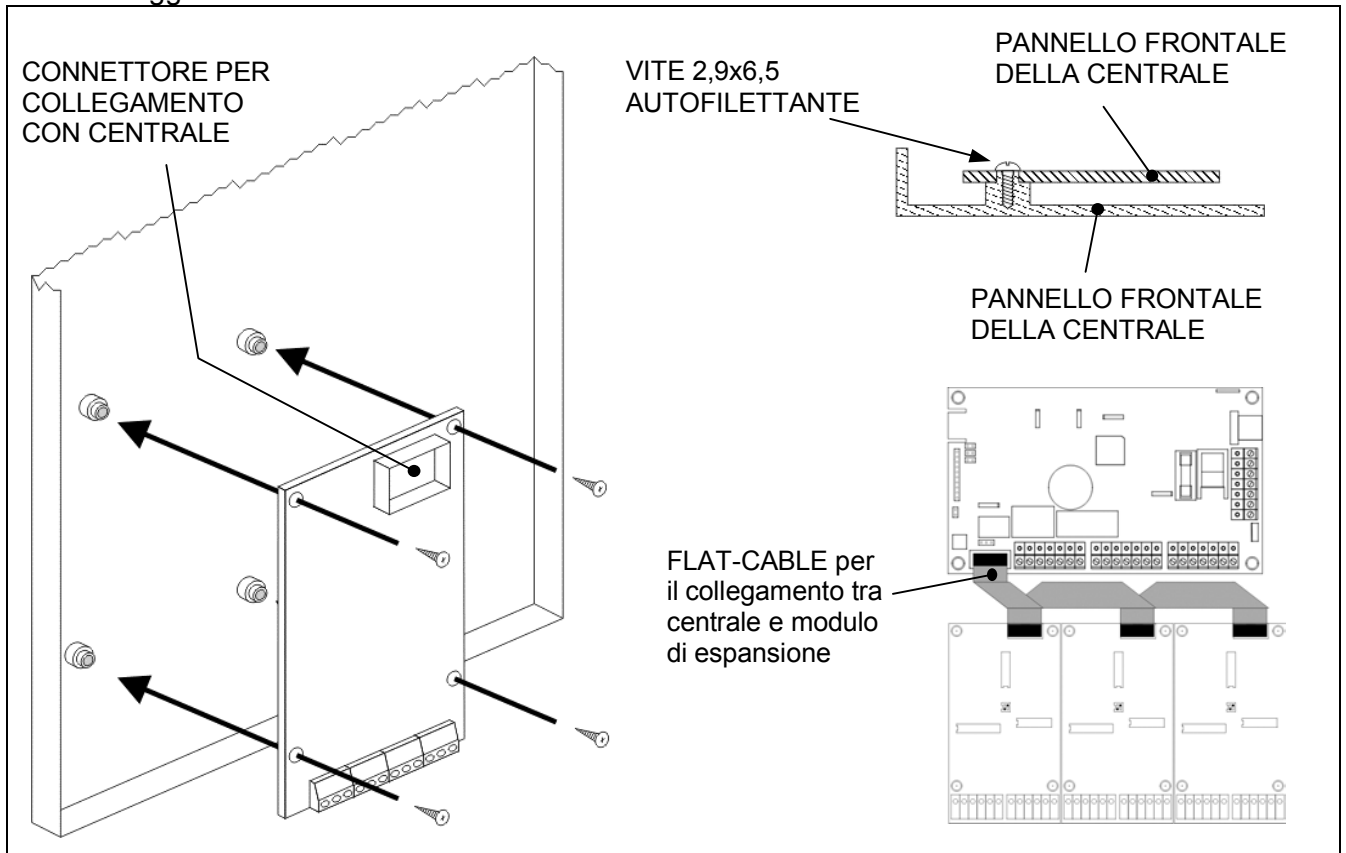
Inserimento, fissaggio e collegamento elettrico del modulo di espansione
